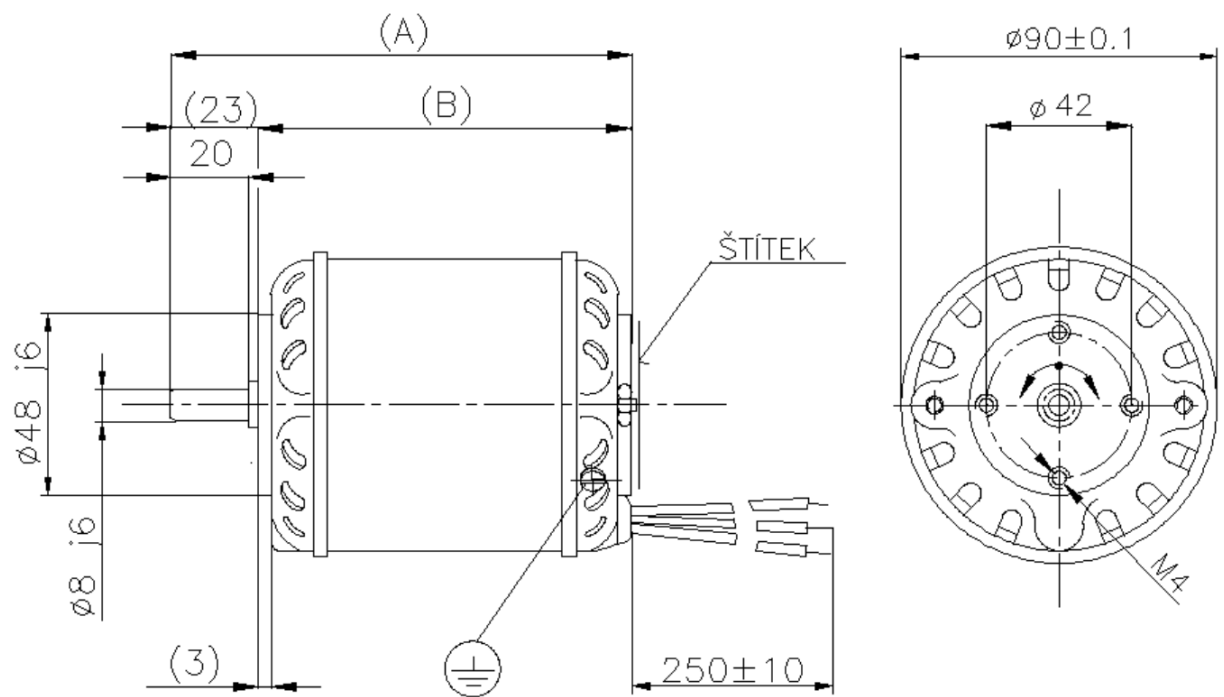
Габаритні та приєднувальні розміри двигуна
